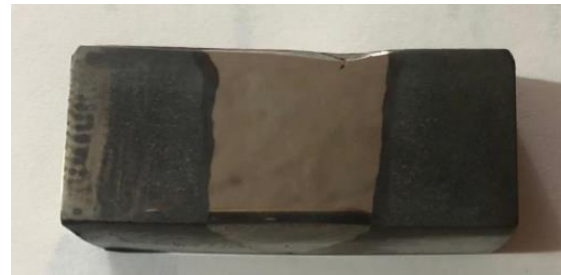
Muestra de soldadura NIQ MANG después del ataque químico.
